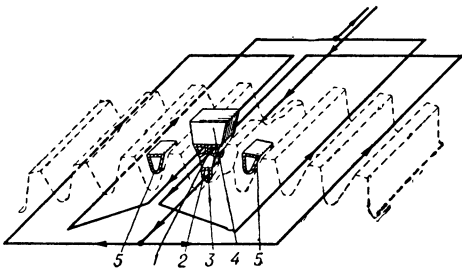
Схема индуктора для нагрева впадины между зубьями шестерни: 1 и 2 — индуктирующий провод; 3 — промежуточный магнитопровод; 4 — магнитопровод; 5 — охлаждающая пластина для предотвращения нагрева обратной стороны зуба.
